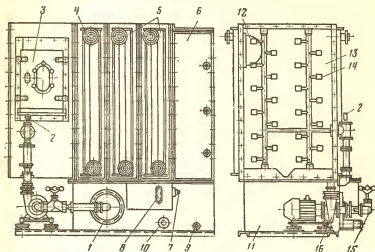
Типовой поверхностный орошаемый воздухоохладитель.
